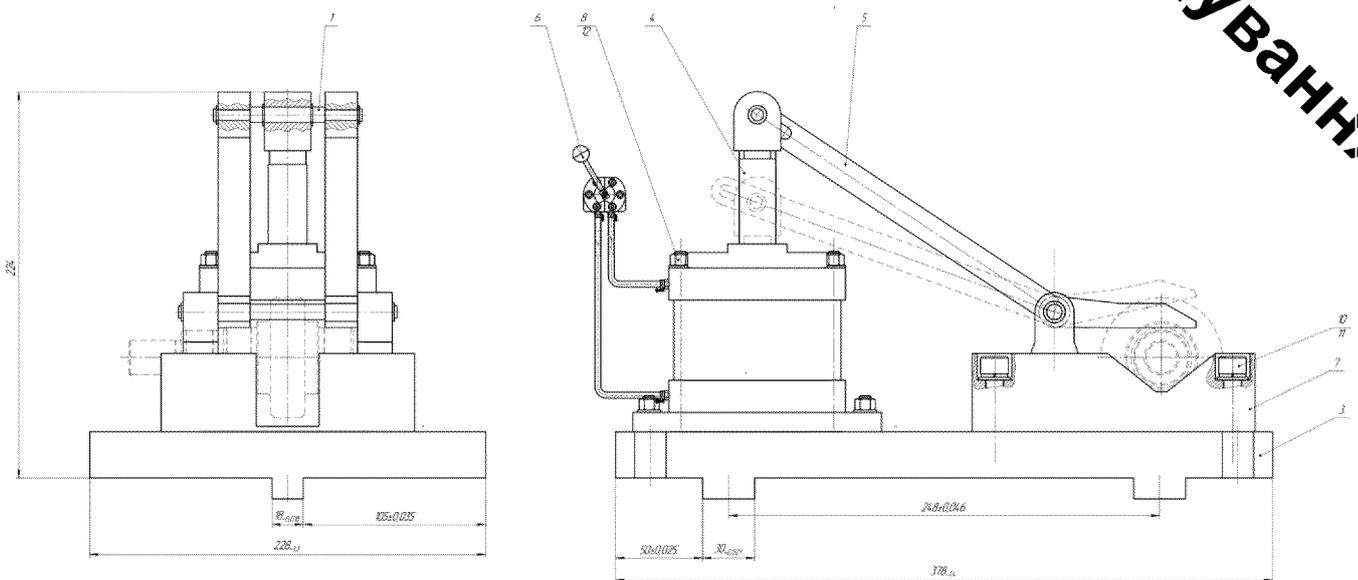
Принципова схема спеціального пристрою для фрезерування пазу
